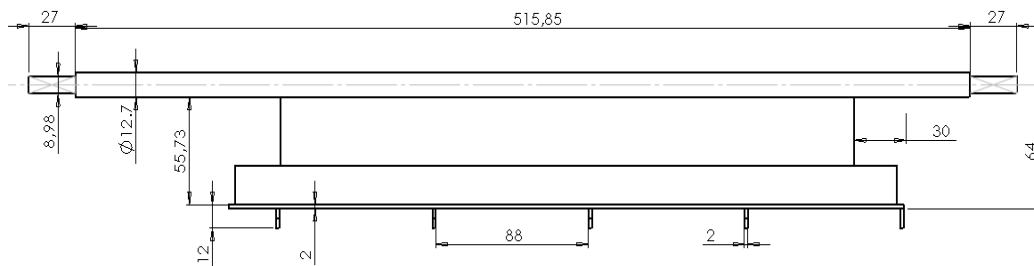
Dimensiones del Eje-Sufridera del conjunto dos.
